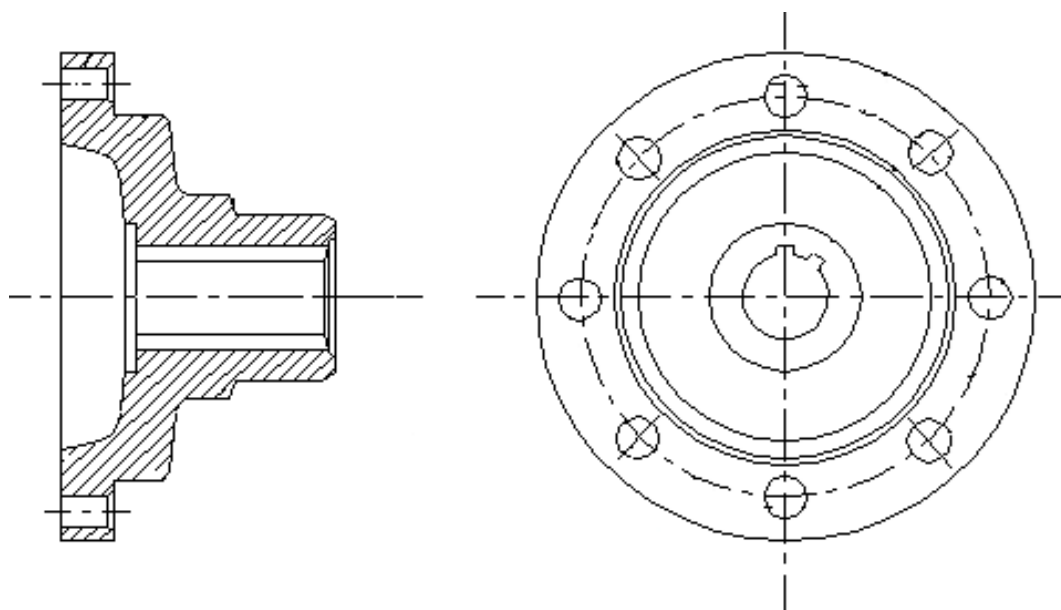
Эскиз детали, фланец раздаточной коробки УАЗ Hunter
